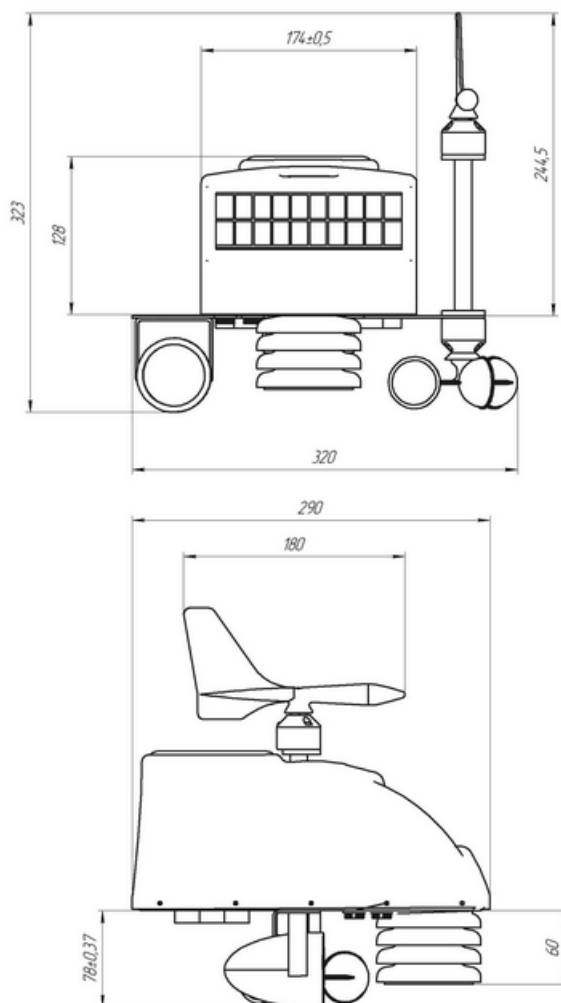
Внешний вид и габаритные размеры станции «СОКОЛ-М1»
